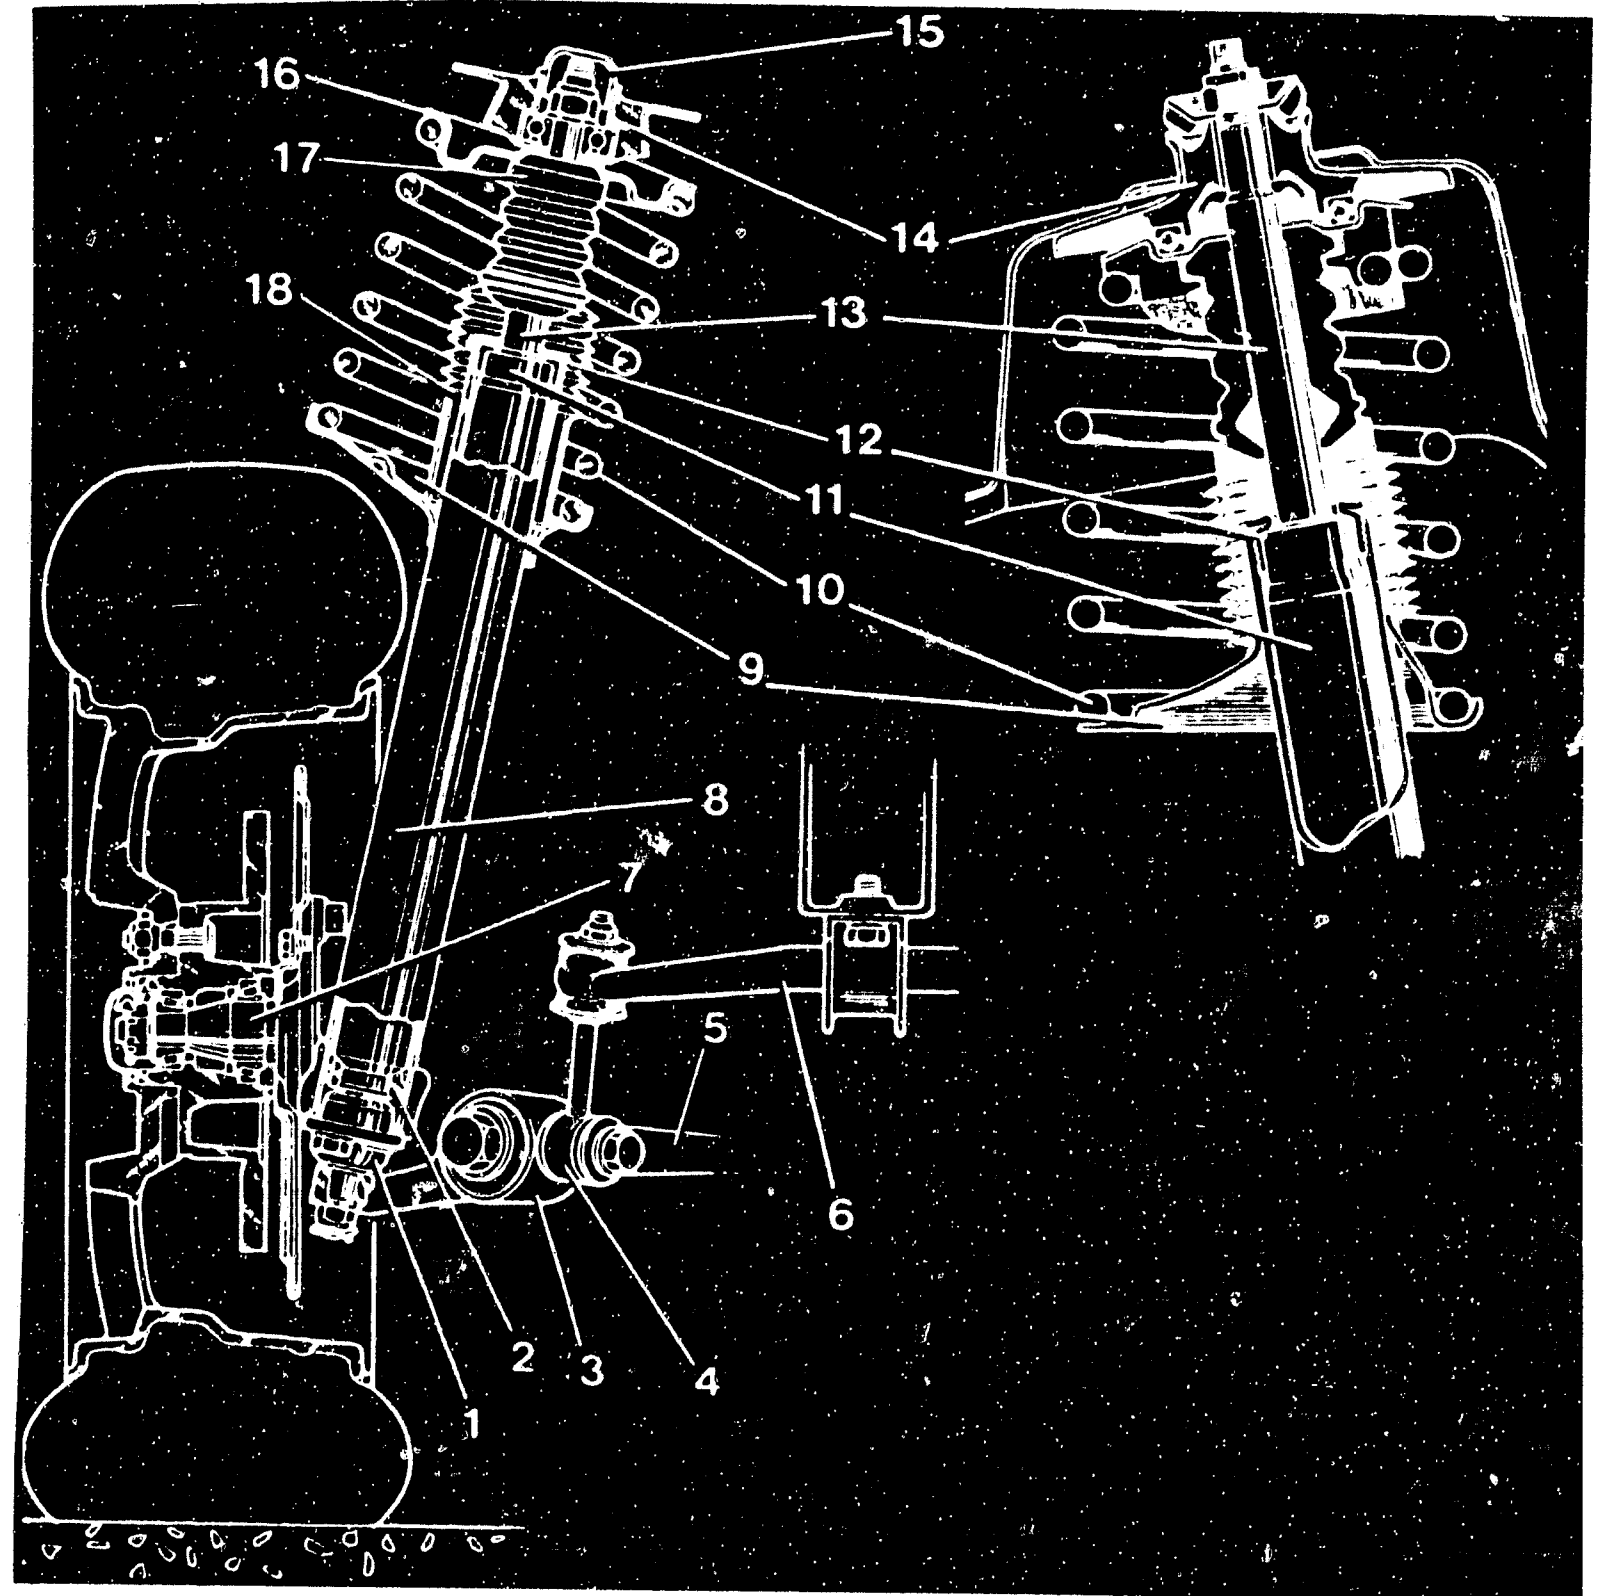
Querschnitt durch die Vorderradaufhängung. Das Bild rechts zeigt die ab 1985 eingesetzte Version der oberen Federbeinlagerung. 1 Kugelgelenk – 2 Sitzring für Stossdämpfer – 3 Querlenker – 4 Reaktionsstab für Querstabilisator – 5 Querlenkerstrebe – 6 Querstabilisator – 7 Achsschenkel – 8 Federbeinrohr – 9 Untere Federauflageplatte – 10 Schraubenfeder – 11 Stossdämpfer – 12 Schraubring – 13 Stossdämpfer-Kolbenstange – 14 Oberes Federbeinlager – 15 Schutzklappe – 16 Obere Federauflageplatte – 17 Gummipuffer – 18 Stossdämpfer-Schutzhülse.
